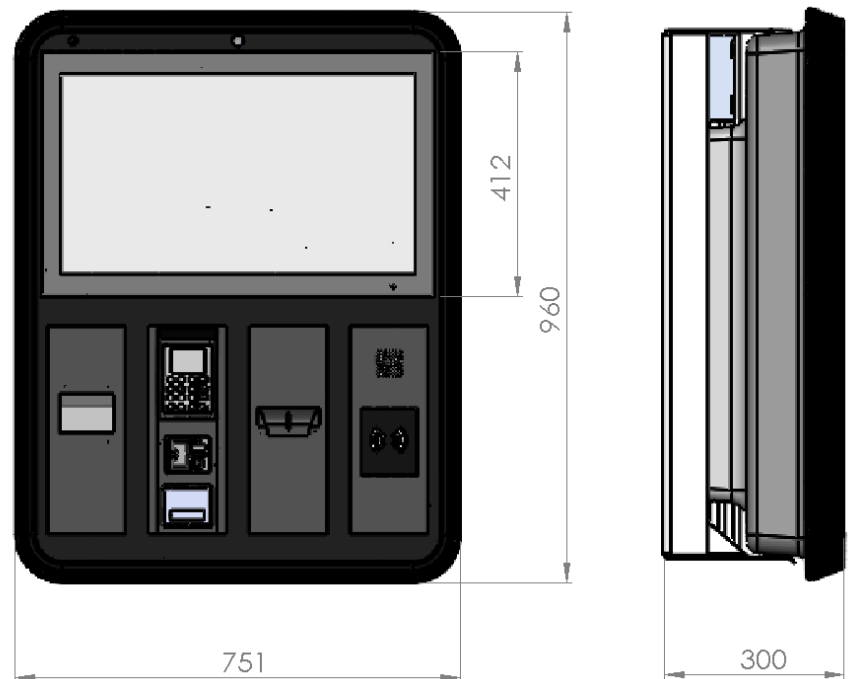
PAY FRAME 600, con cornice luminosa, dimensioni in mm
